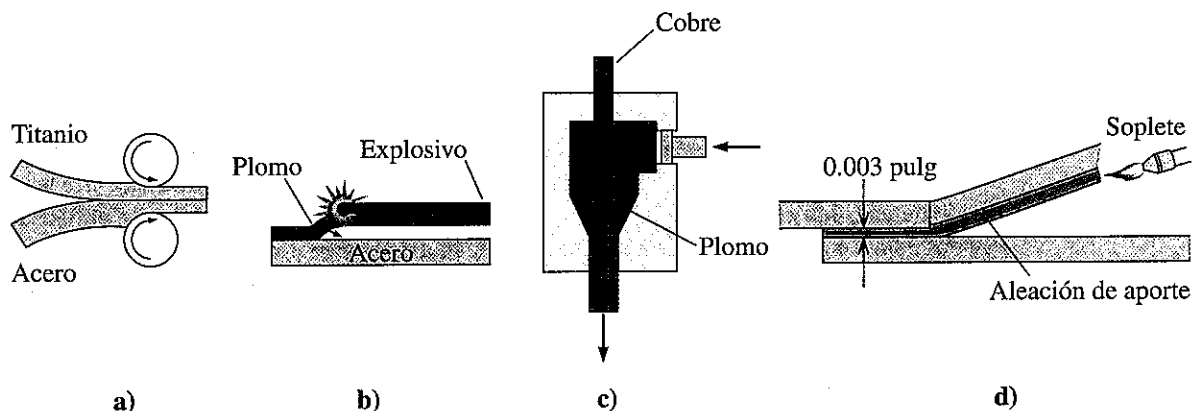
Técnicas para producir compuestos laminares: a) unión por laminación, b) unión por explosión, c) coextrusión y d) soldadura con aporte.
